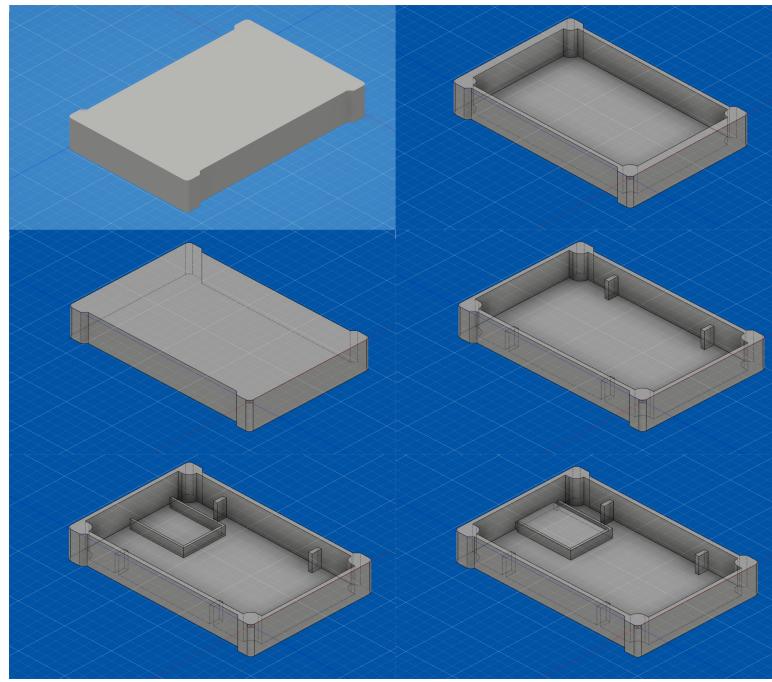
Proceso del diseño del molde inferior parte 1
